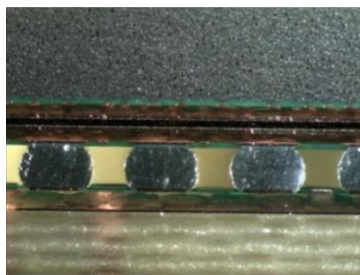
Běžné rozměry pouzder typu BGA [9]
